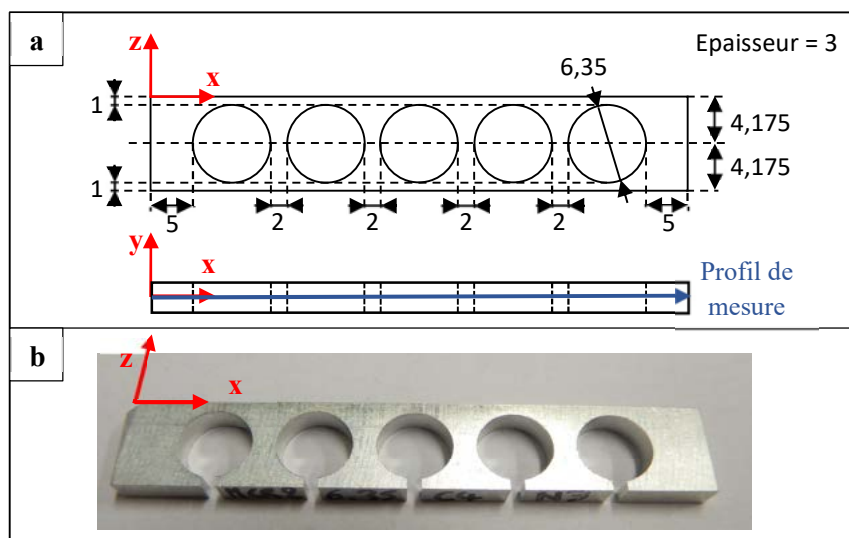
Géométrie d'éprouvette d'analyse des contraintes résiduelles par la technique de HOCT (dimensions en mm)
